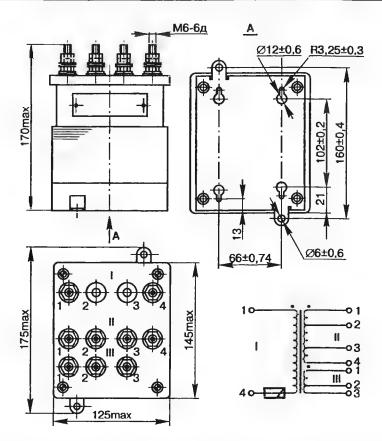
Схема соединения обмоток пожаробезопасного трансформатора ПОБС-2МП и его присоединительные и габаритные размеры
